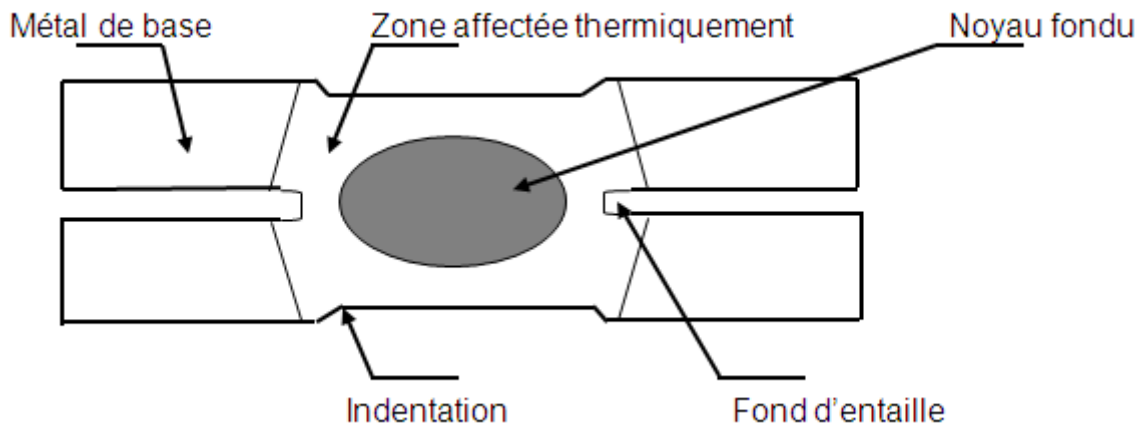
Zones principales d'un cordon de soudure par fusion
